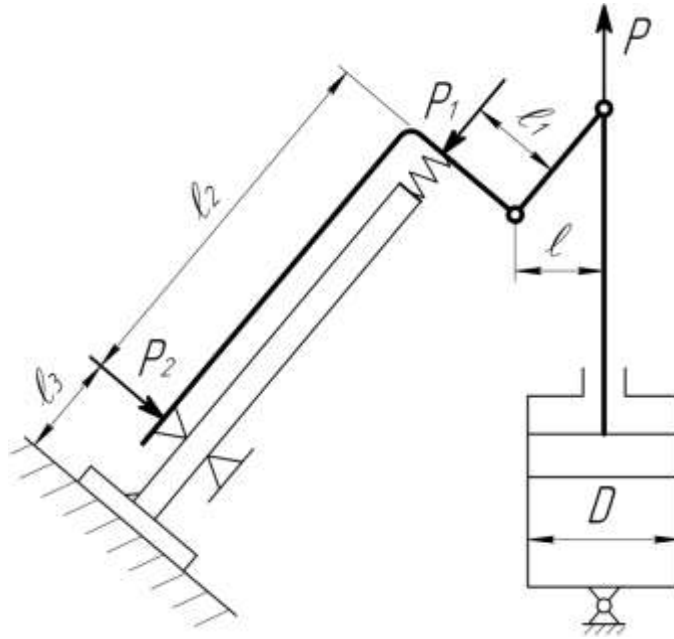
Схема рычажного прижимного устройства для сборки тавровых балок
